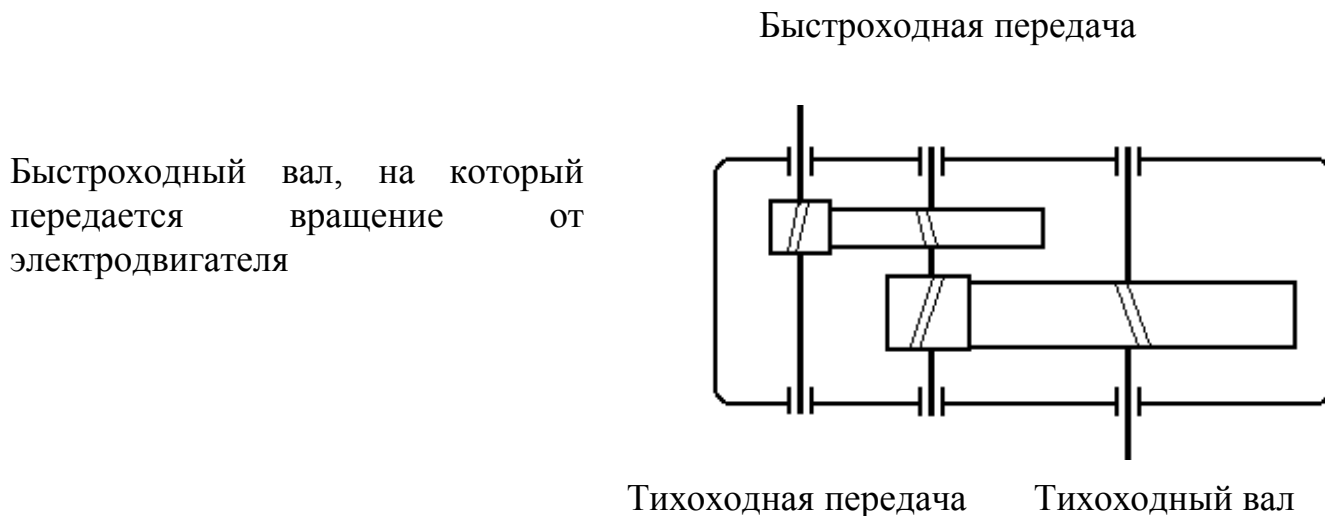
Цилиндрический двухступенчатый редуктор по развернутой схеме с косозубыми колесами
